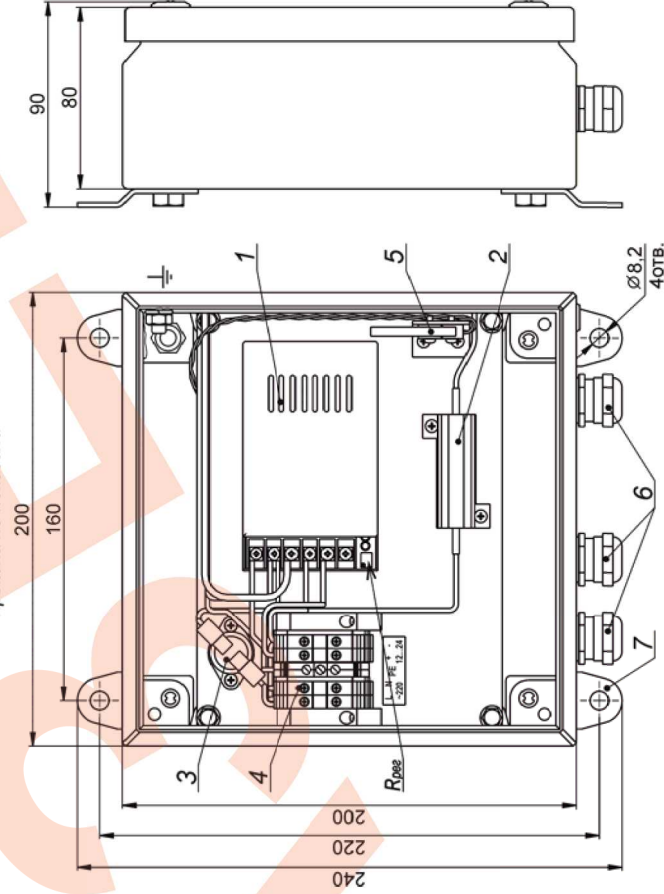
Устройство, габаритные и установочные размеры БПУ-1
